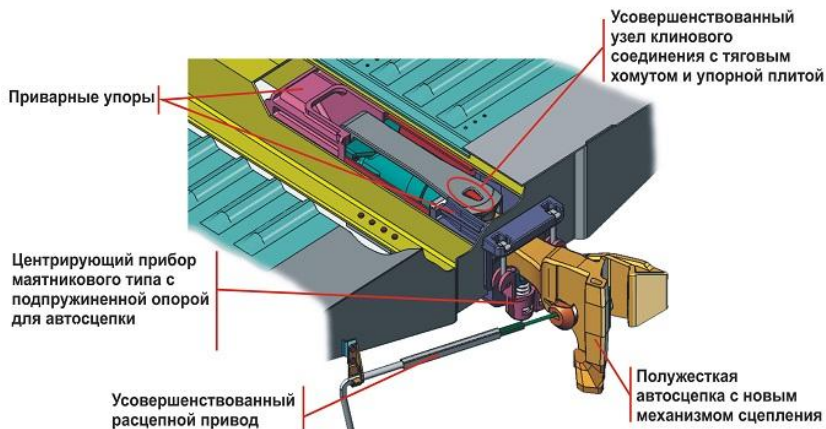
Общий вид автосцепного устройства с автосцепкой СА-4 и расцепным приводом с телескопическим рычагом
